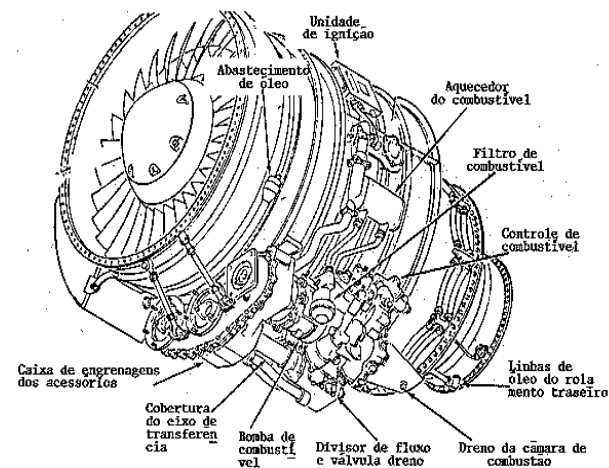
Seção de acessórios de um motor de fluxo axial.
